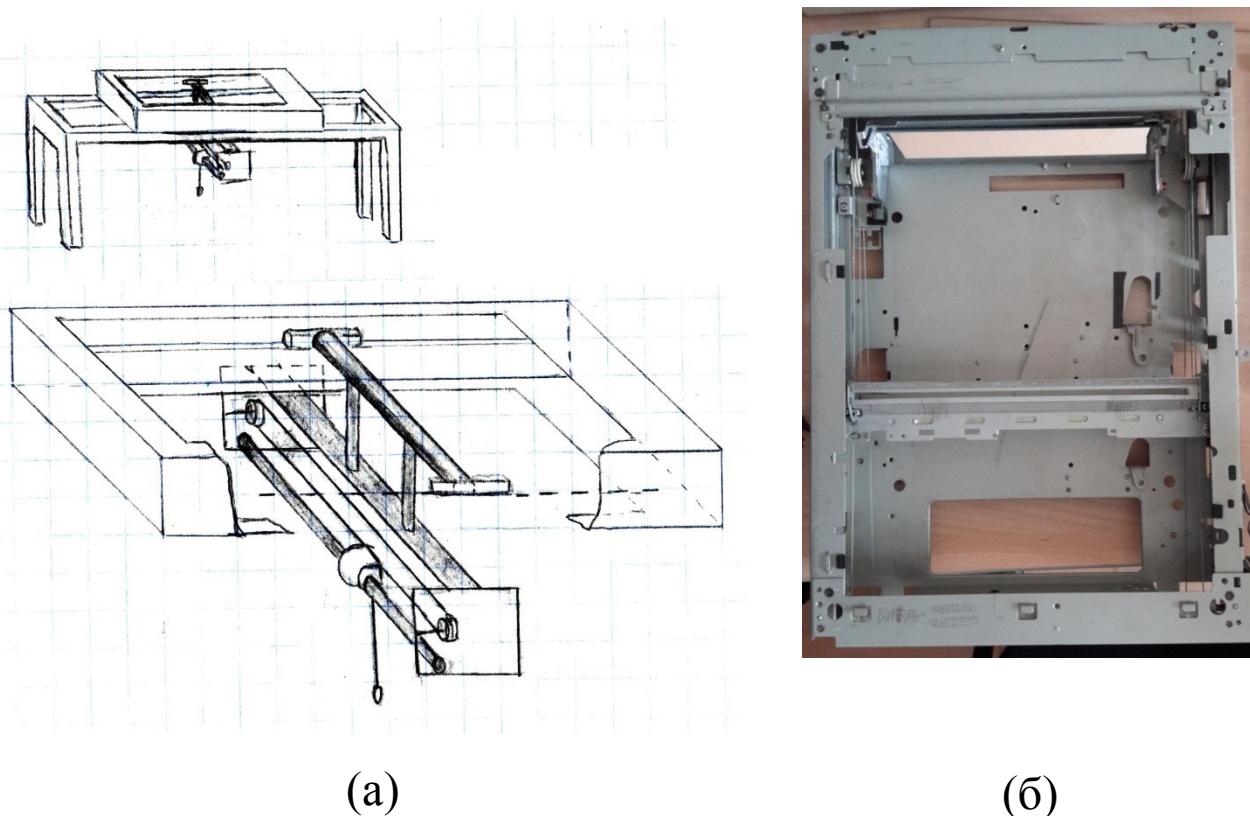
Первая принципиальная схема установки на основе подвижных частей сканера и принтера. (б) Извлеченная из сканера система перемещения сканирующей каретки – предполагаемая основа разрабатываемой установки.
